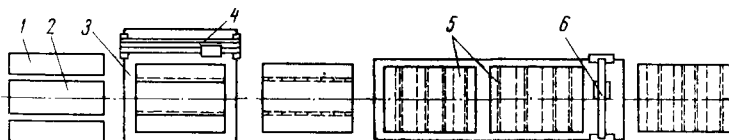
Схема поточной линии сборки и сварки секций крыши электровагона
